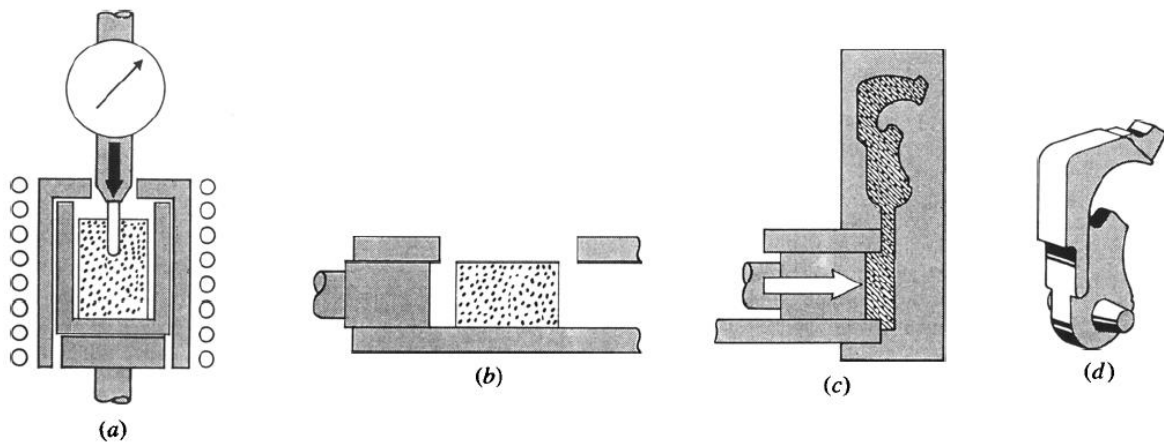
Principe du thixomoulage. (a) Chauffage jusqu'à l'état semi-solide, (b) chargement du lopin SS dans la machine à mouler, (c) moulage, (d) pièce finie.
